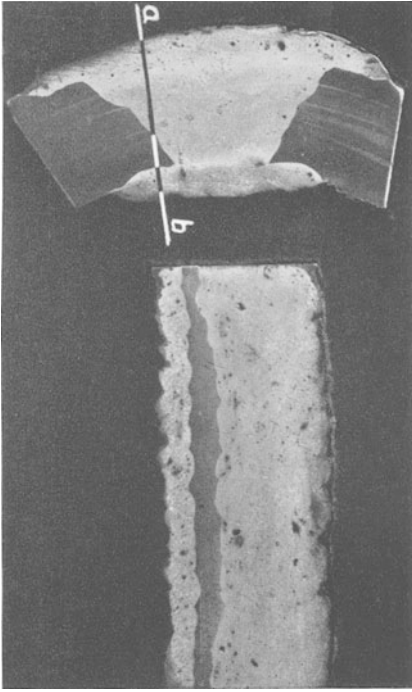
Schweißnaht eines Wasserrohrs in einem Torpedobootskessel.
